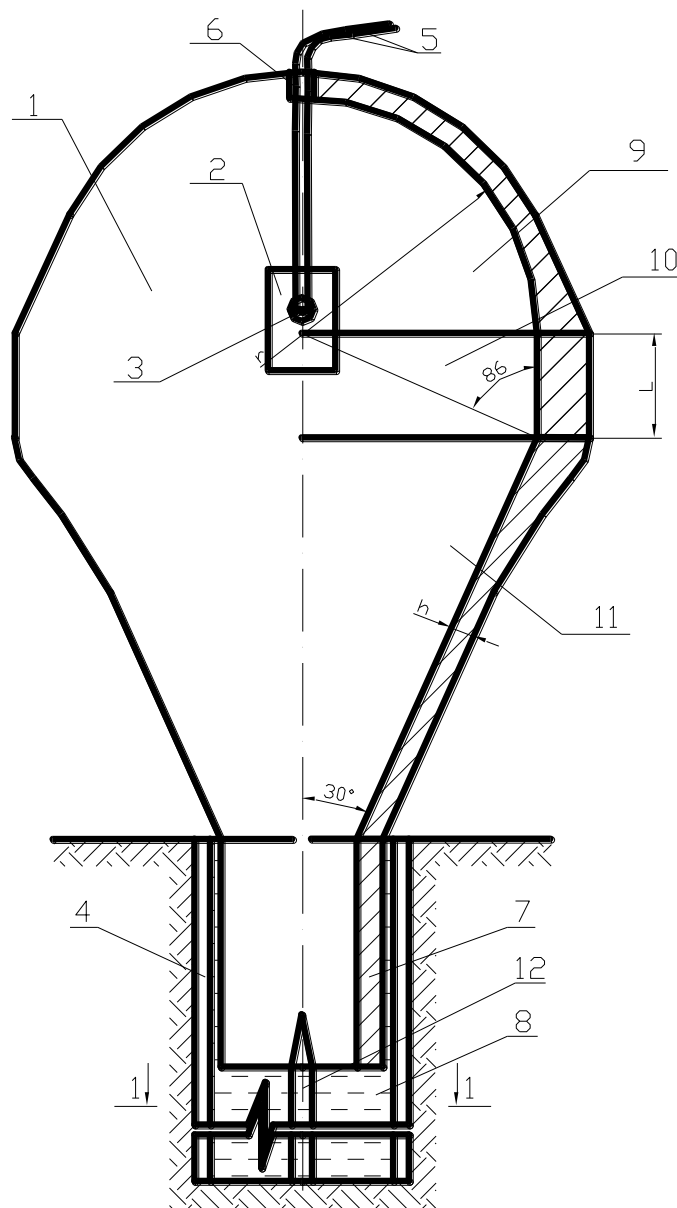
Загальний вигляд установки для блочного відділення каменю
